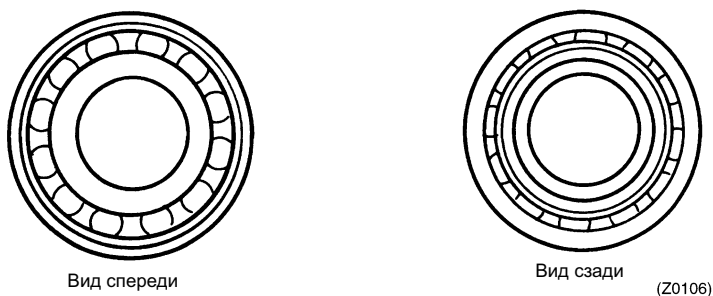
Передняя и тыльная стороны шарикоподшипника с коническими опорами
